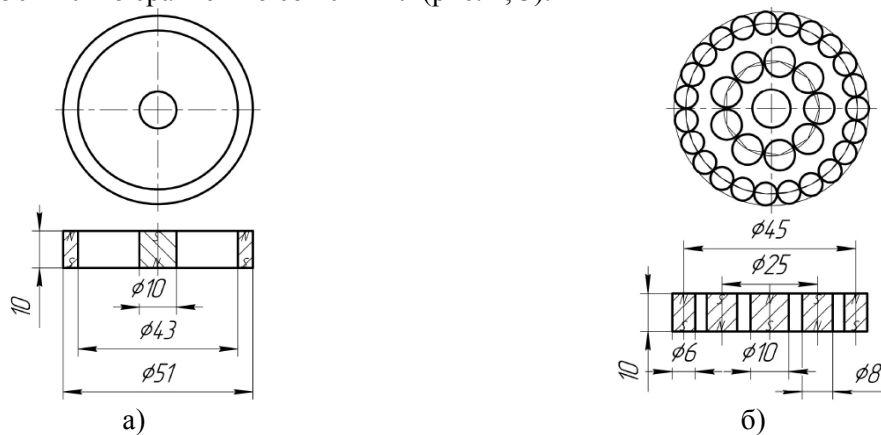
Конструкции магнитных систем магнетрона НМСА-52М: а) с цилиндрическими и кольцевым магнитами; б) с двумя областями плазмы.
